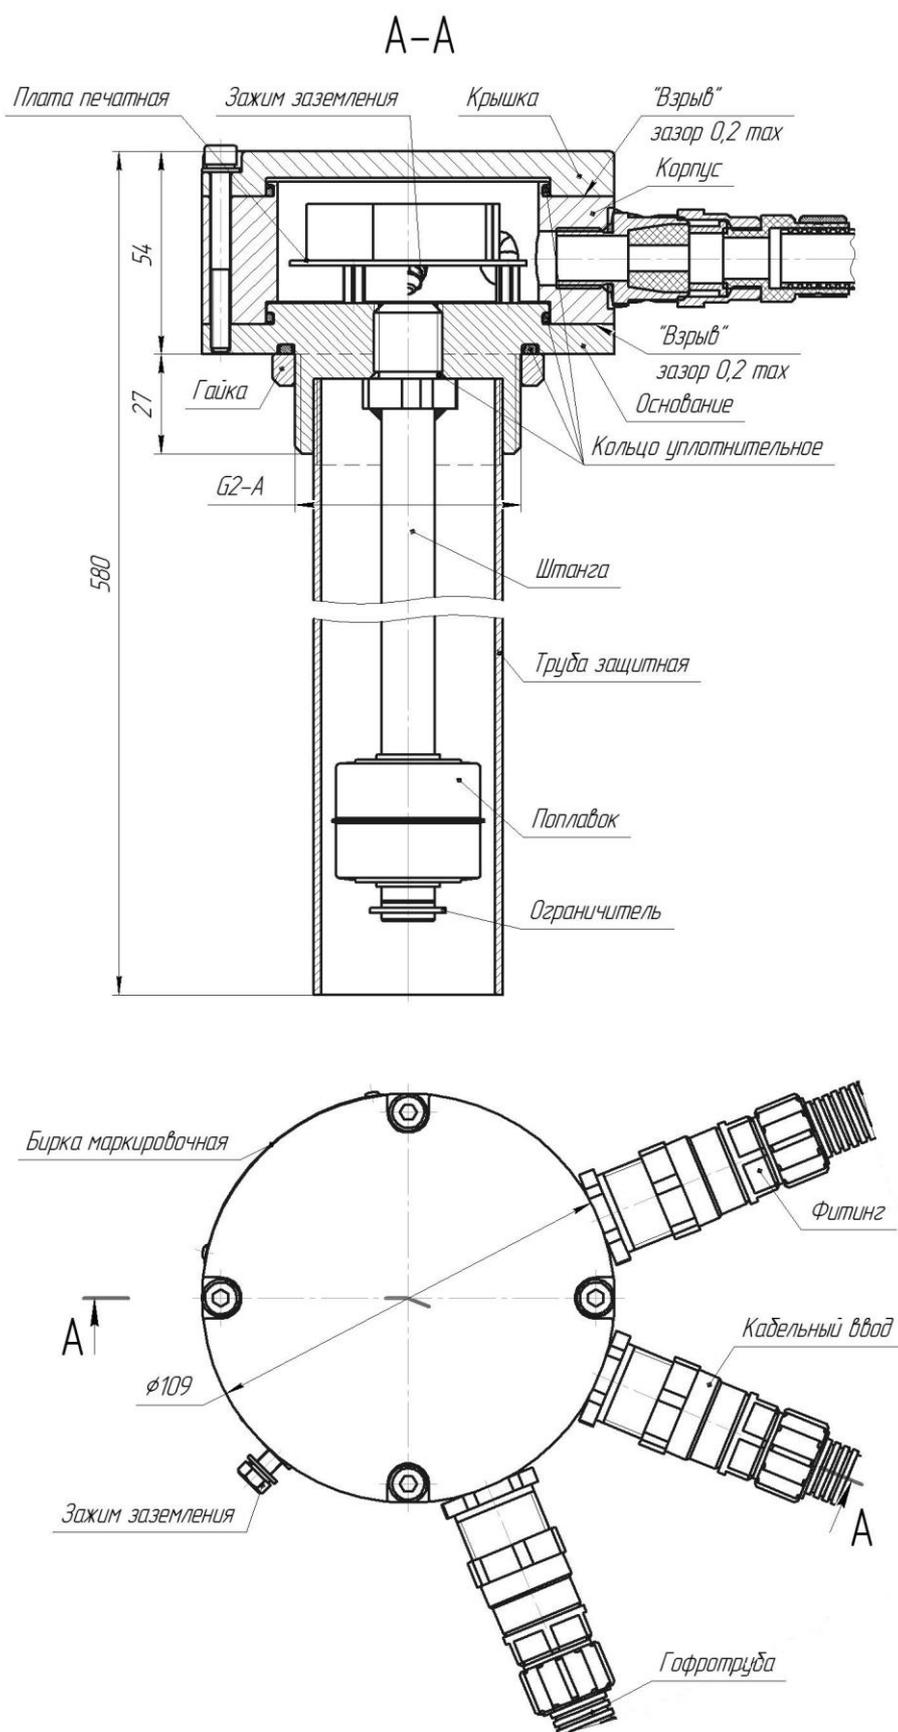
Габаритные и присоединительные размеры ДЛЮК-У-1
